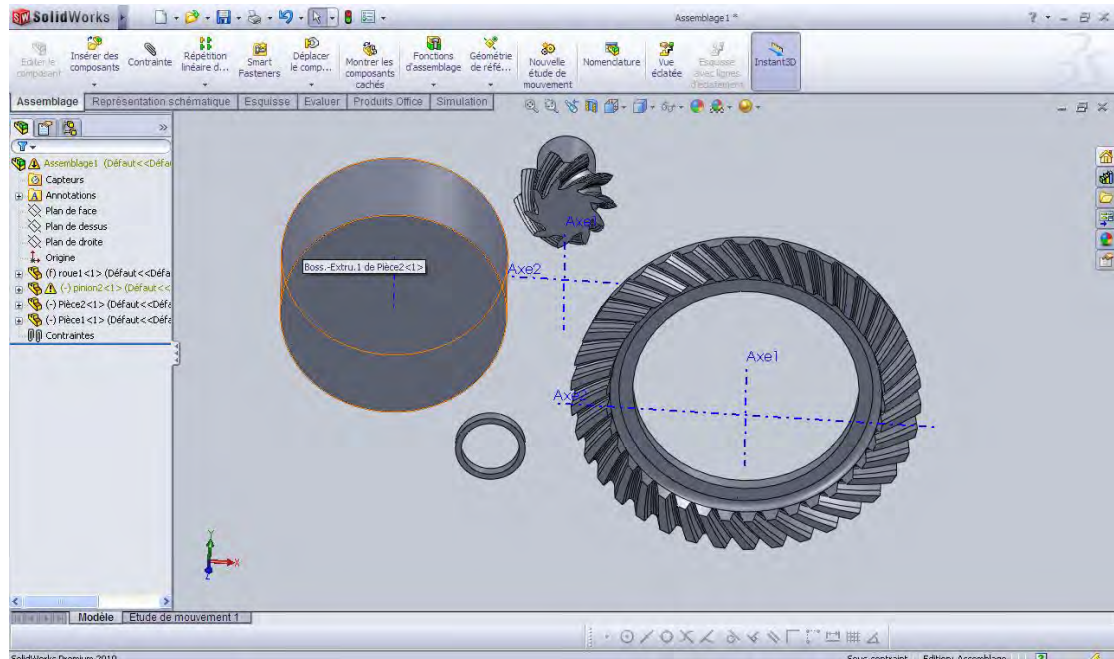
Construction de l'assemblage phase 1 : importation des pièces
